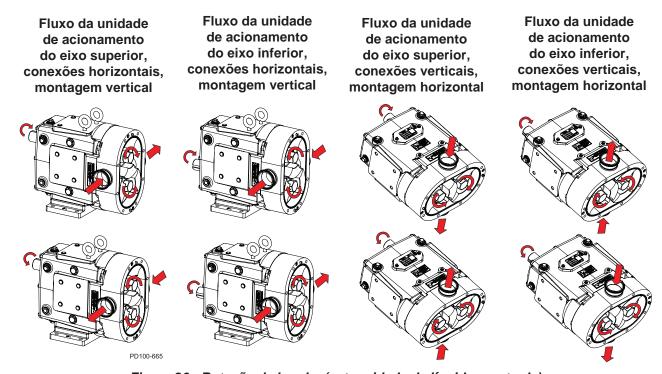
Rotação da bomba (extremidade de líquido mostrada)
